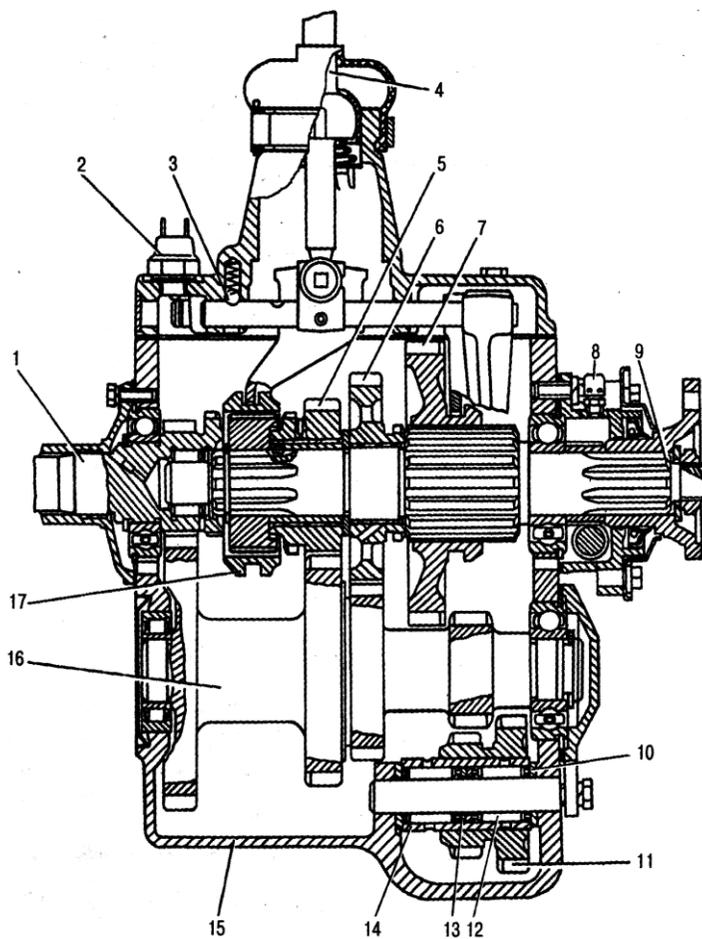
Коробка передач автомобиля ГАЗ-3307:
